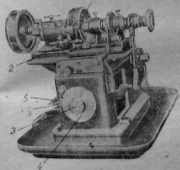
Автомат Петерман для фрезеровки квадратов.
